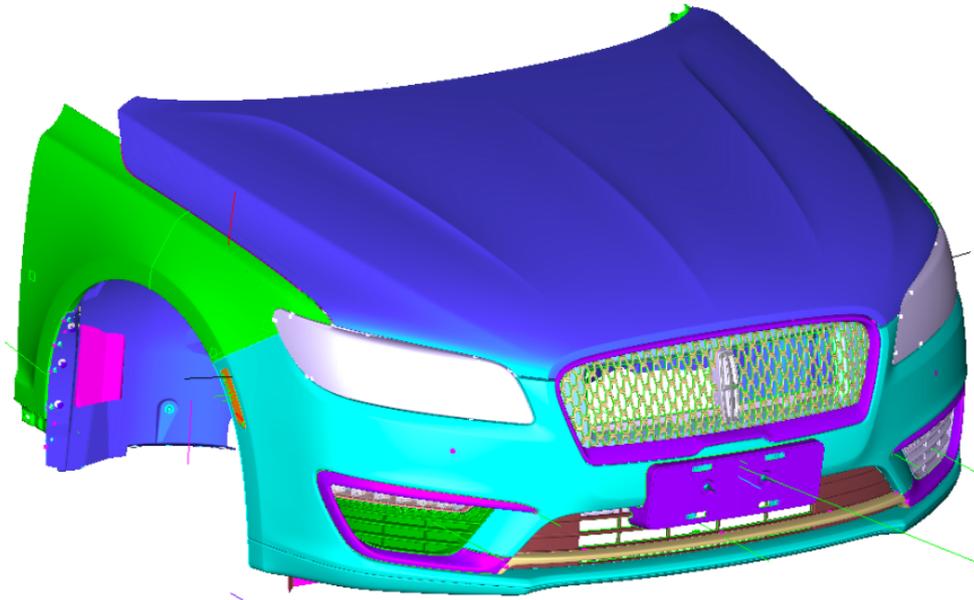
Contexto de apariencia de la fascia: Sistema de iluminación, piezas metálicas estampadas (salpicaderas y cofre), lodera de salpicadera y emblema de la compañía
